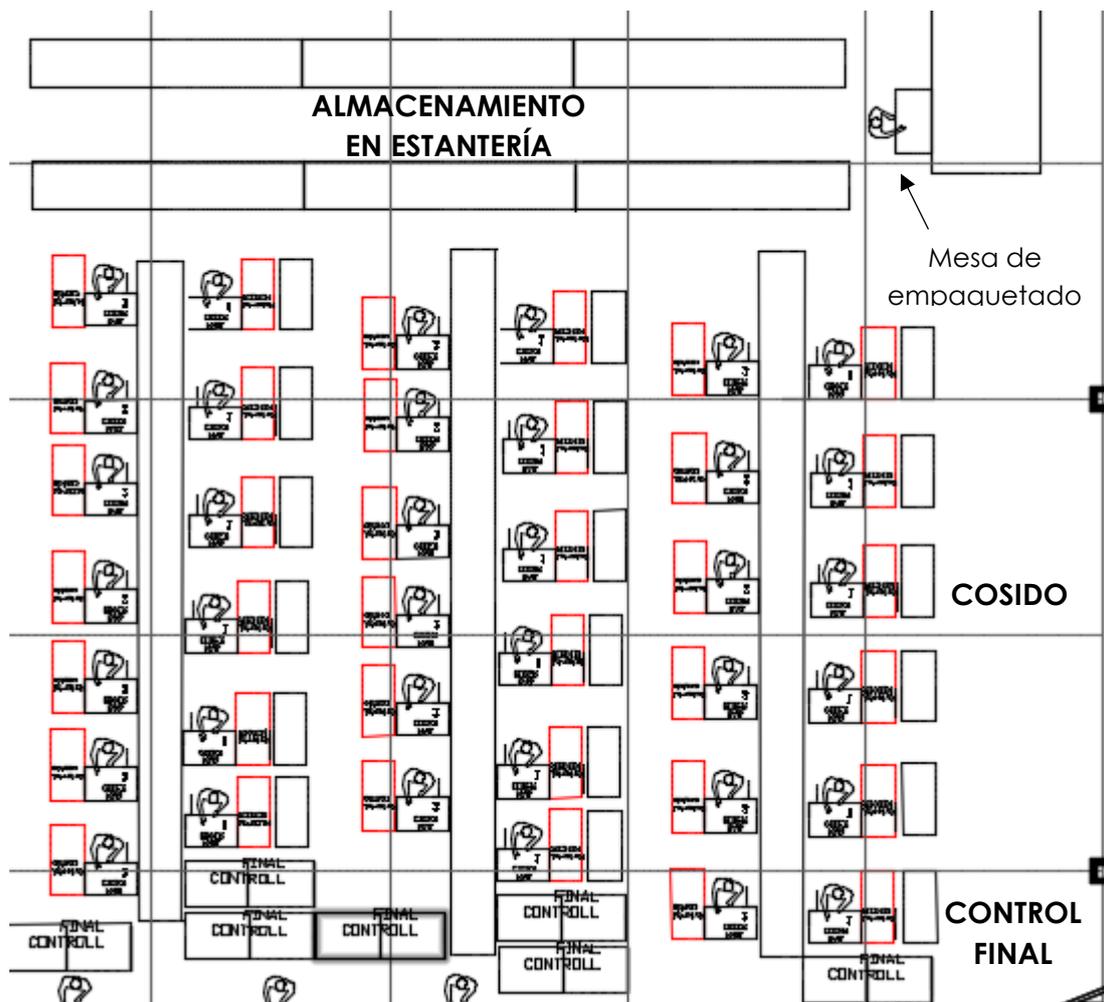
Layout actual: Zona 2. Fuente: Elaboración propia
